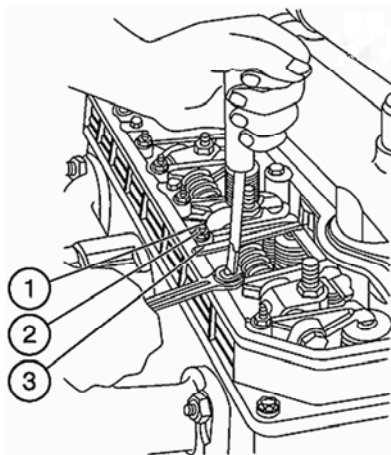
Регулировка зазоров в клапанах двигателя Д-243:
